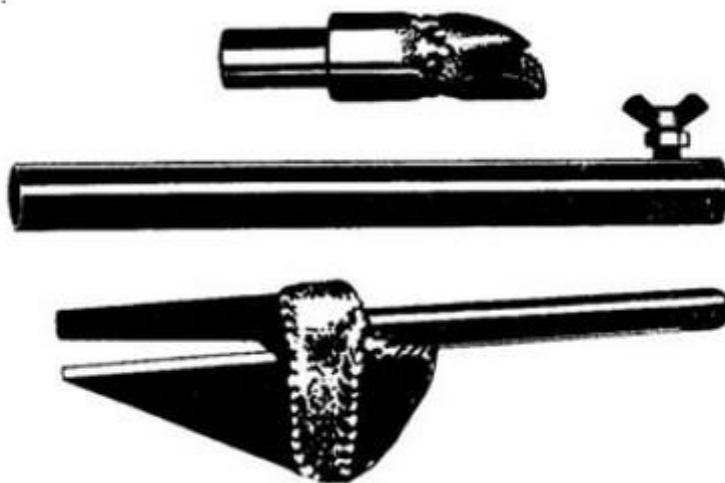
Инструменты, изготовленные по типу консервного ножа
